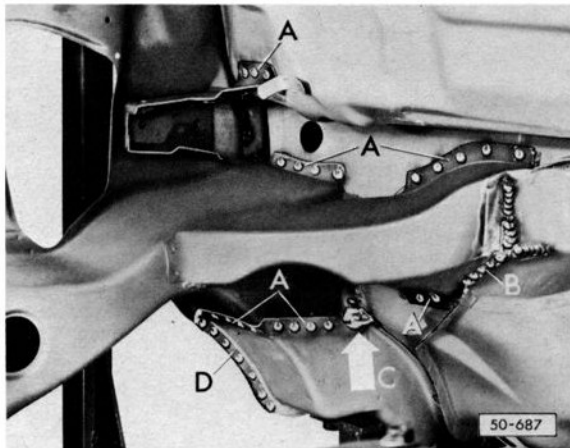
Vorderwagen-Neuteil einschweißen
